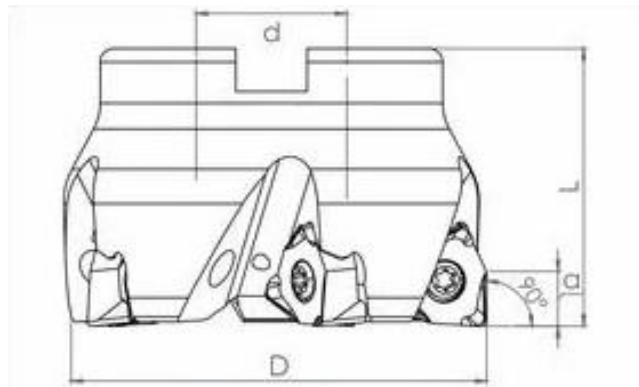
Геометричні параметри торцевої фрези фірми SECO Octomil R220-43-8200-07C
